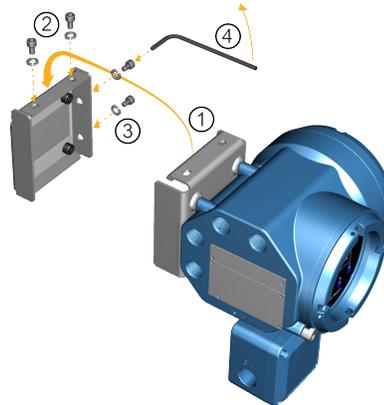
Soporte de montaje en pared y dimensiones para un transmisor de acero inoxidable
